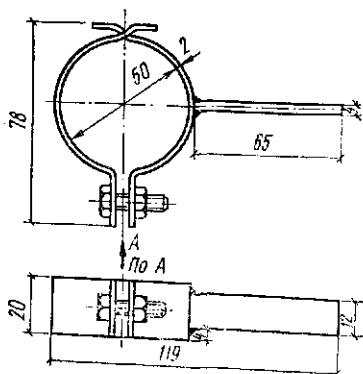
Хомутки типа 41кс (масса 0,18 кг) для крепления полиэтиленовых труб D_y 50 мм к закладным деталям сваркой в санитарно-технических кабин
